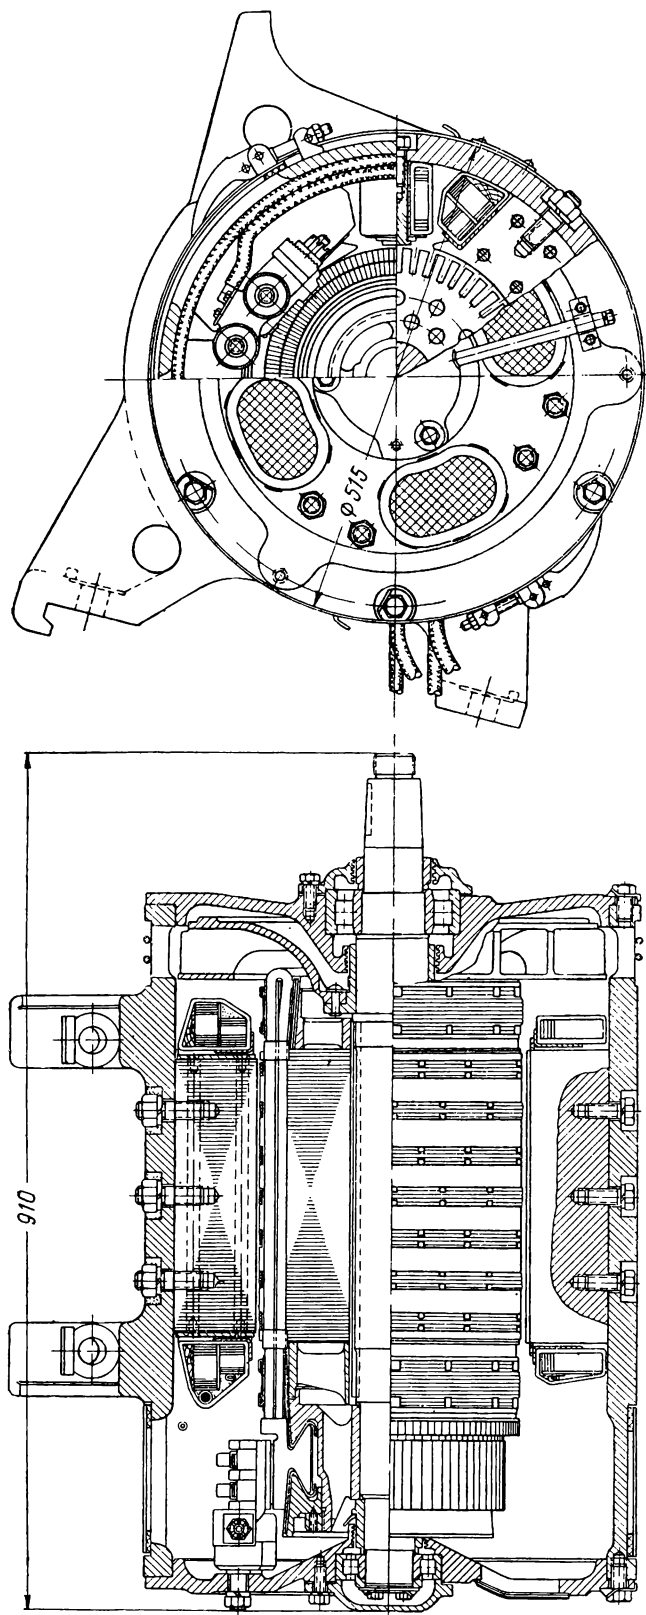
Тяговый двигатель типа ЭДР-10 с двухступенчатым редуктором.
